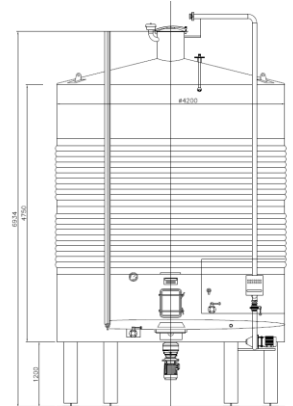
Depósito autovaciante de 65 m³ con fondo plano.
